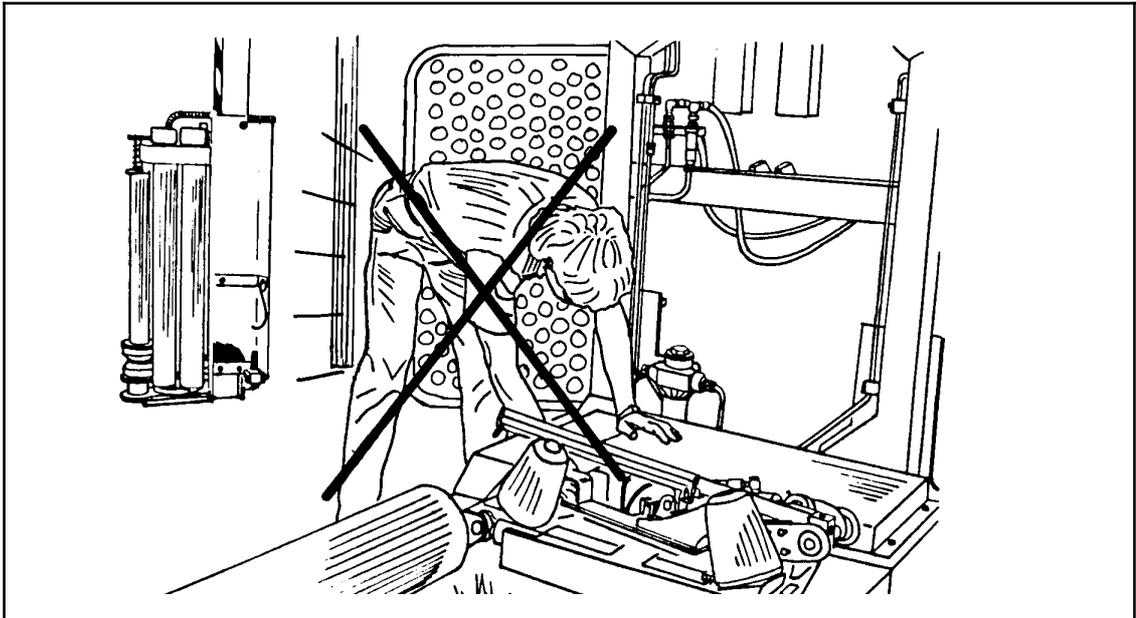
ACHTUNG! Beim funktionstest aufpassen! Wickelarm kann ausschlagen!
